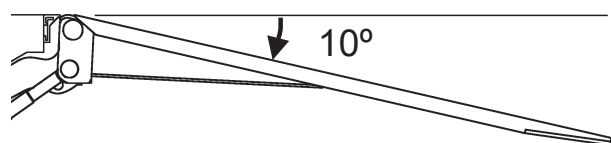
La plate-forme ne doit pas être inclinée à plus de 10° par rapport à l'horizontale
